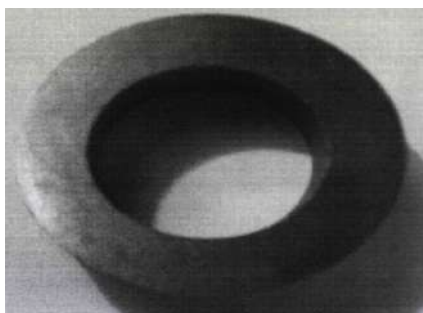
Деталь з чавуну, яка піддавалась окисленню
